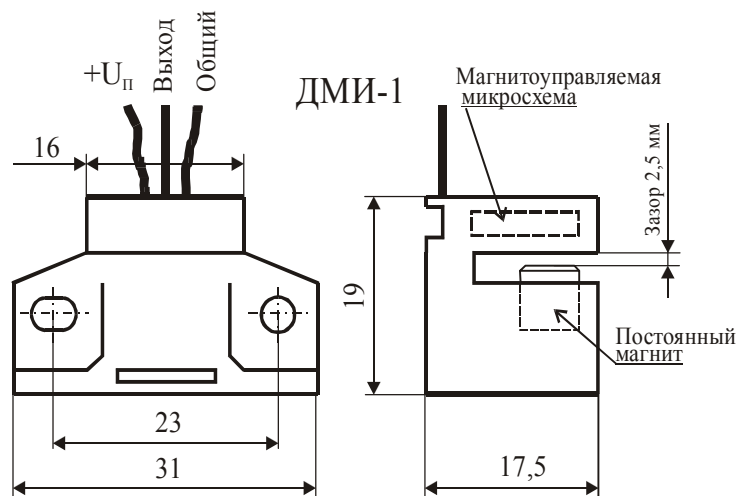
Внешний вид и габариты щелевого магнитного датчика типа ДМИ-1
